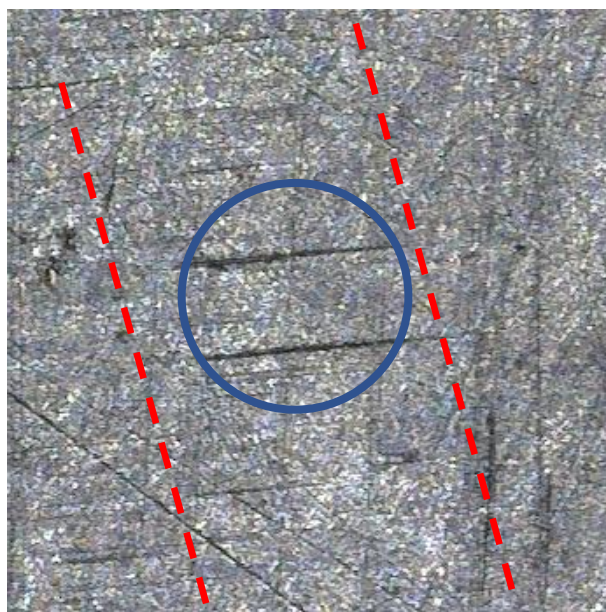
Fotografia da superfície da chapa nº 425 (1700 quinagens)
